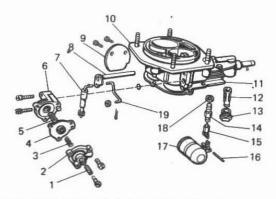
Piezas de la tapa del carburador 2107-1107010:
